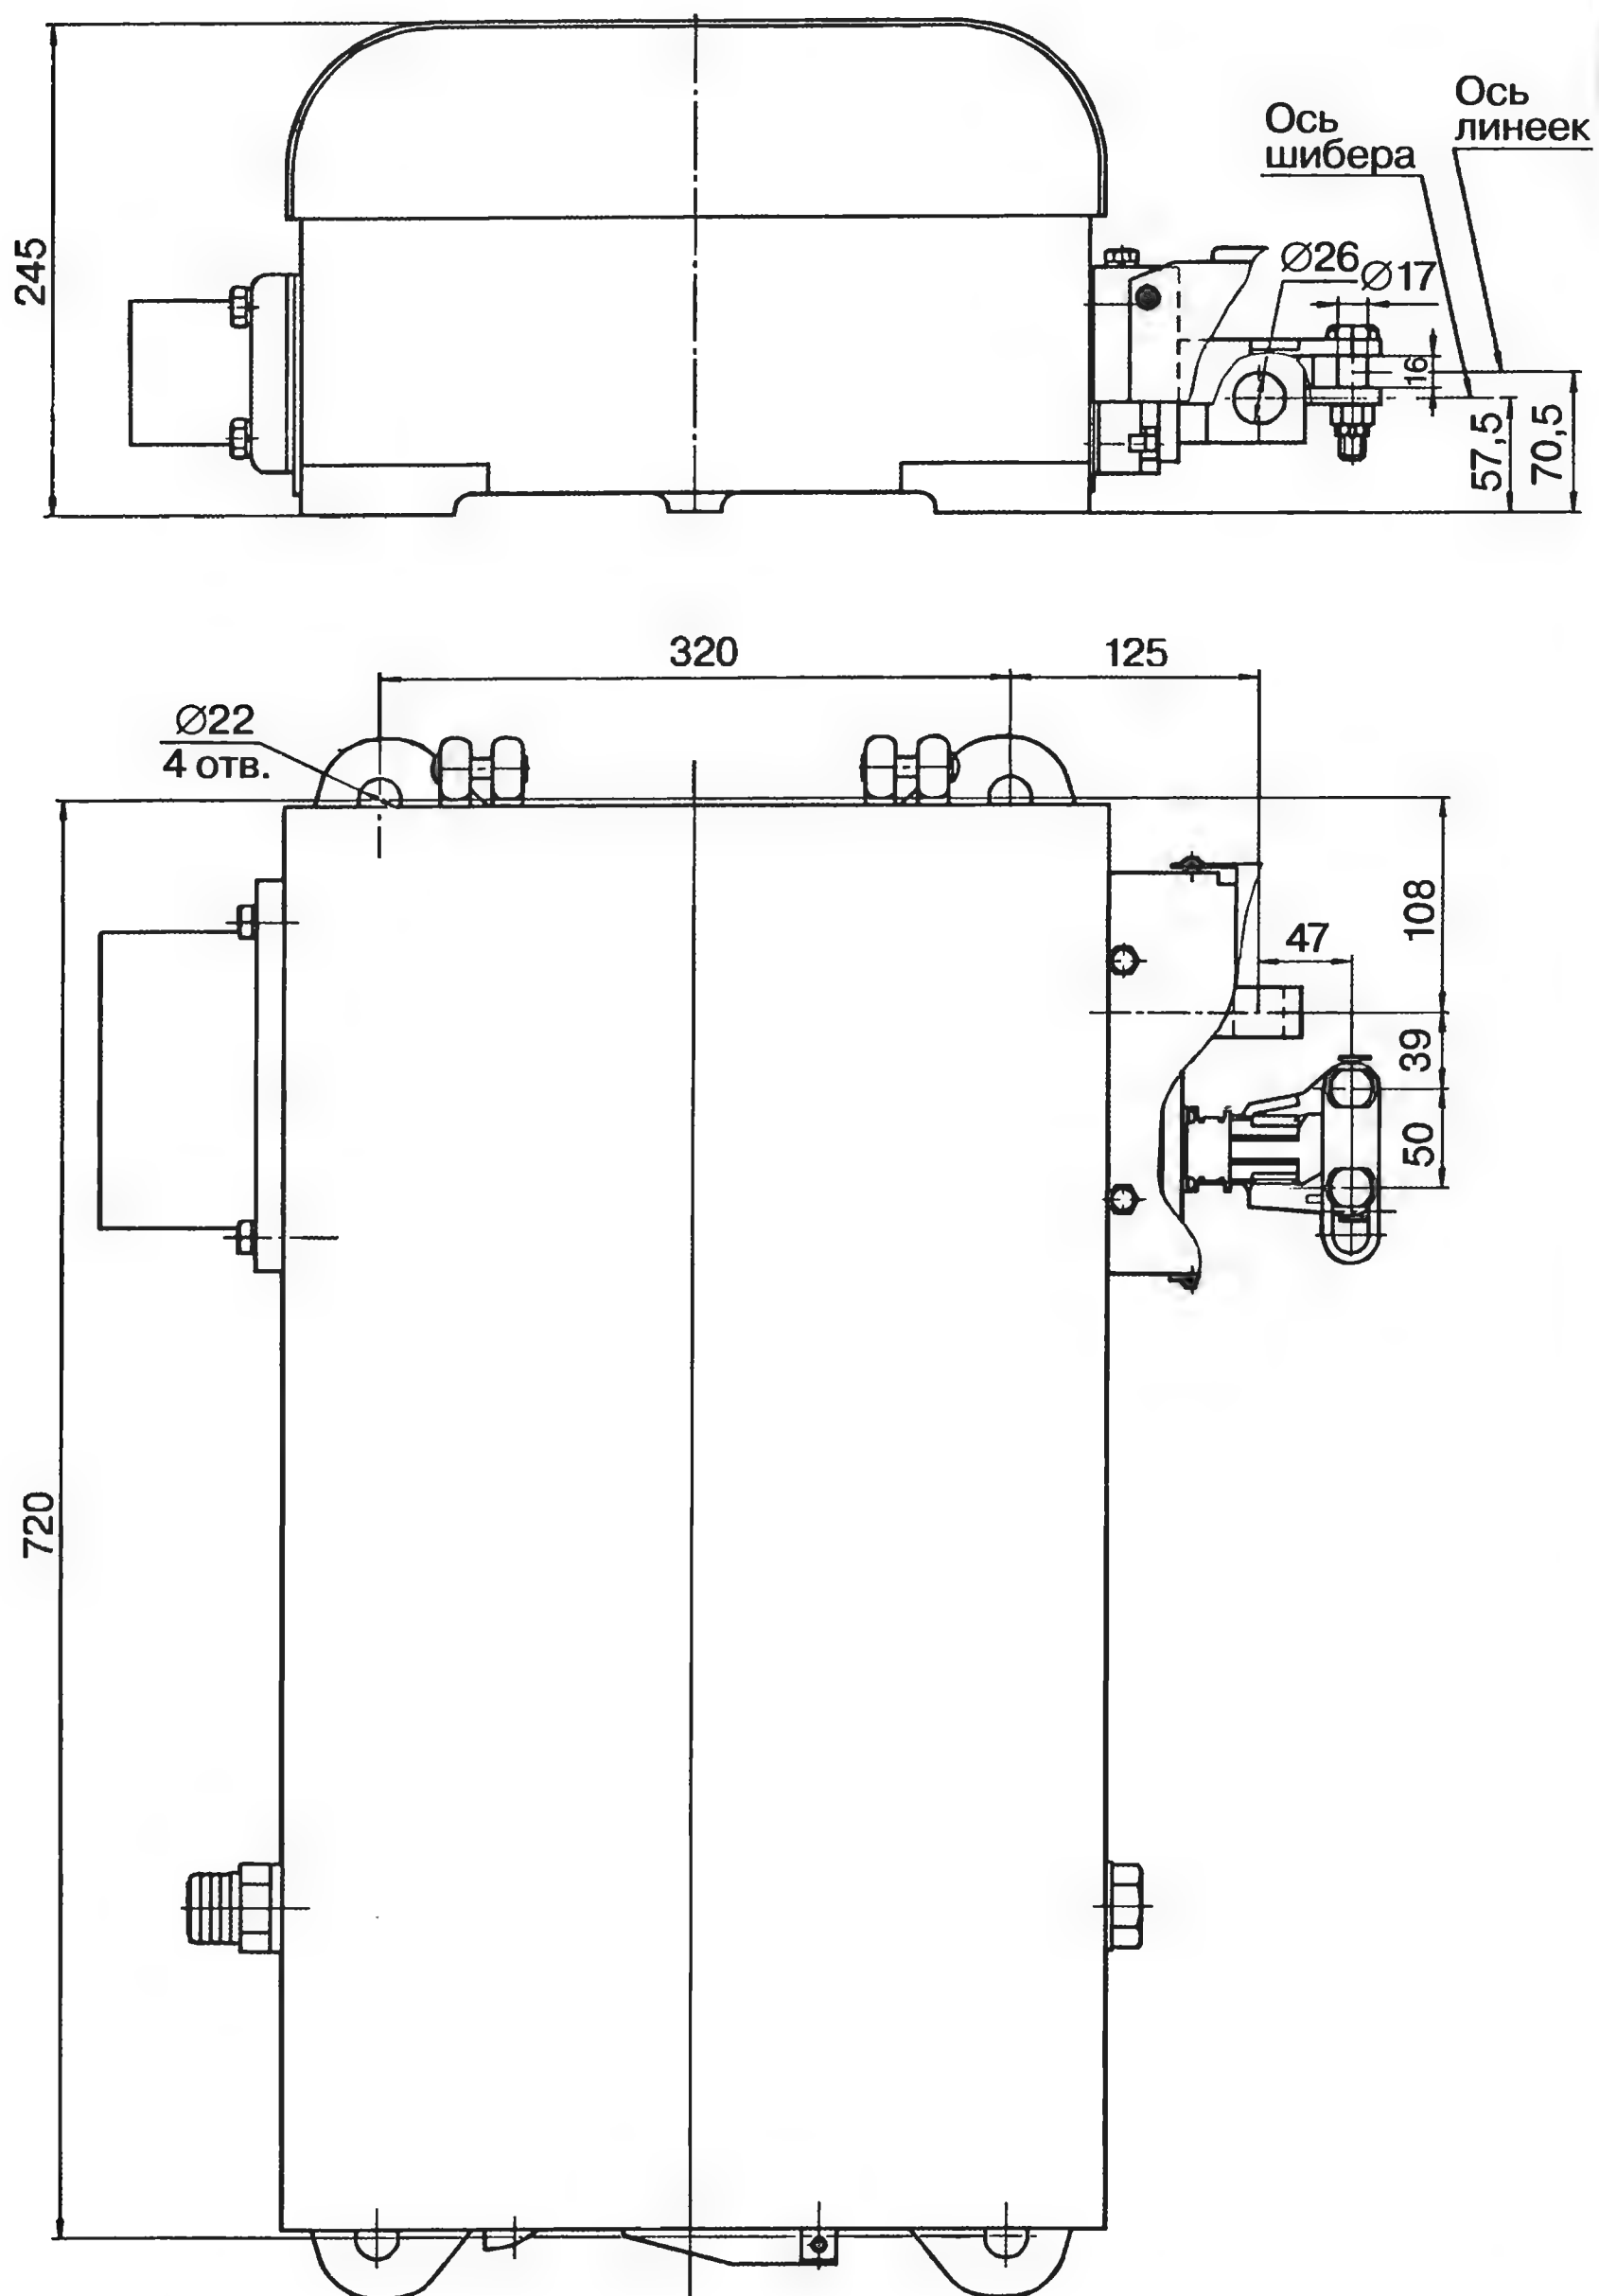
Электропривод стрелочный СП-12Н. Установочные и присоединительные размеры
